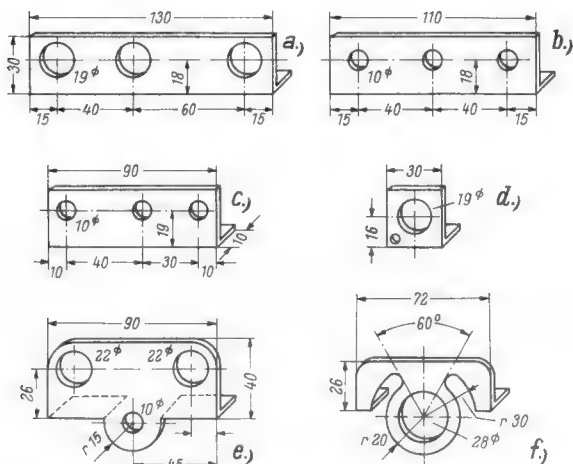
Maßskizze der mechanischen Kleinteile; auch hier sind die Befestigungslöcher weggelassen
